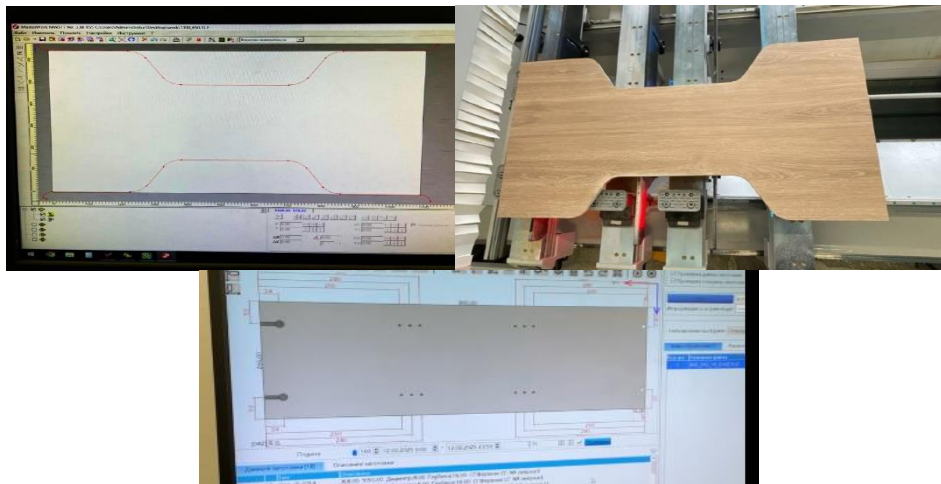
Изготовление детали с помощью станка с ЧПУ, работающего с ИИ
